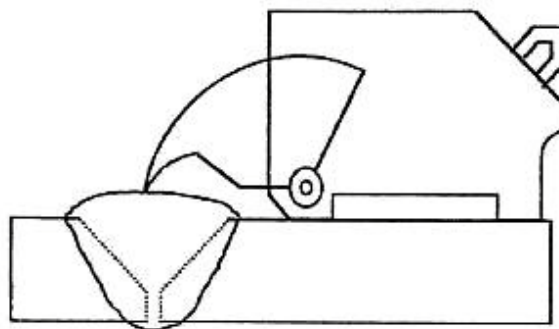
Determinación de la altura del refuerzo de soldadura
